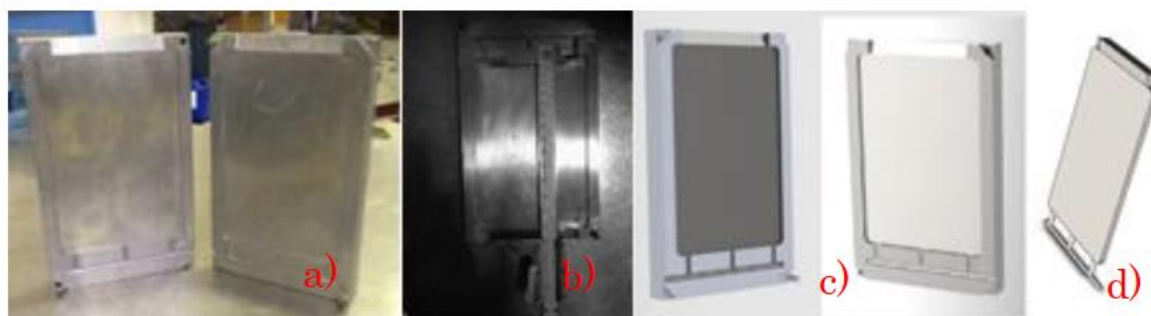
Representação do molde de metal utilizado: a) molde em aço b) e c) medição do molde para obtenção das quantidades de mistura e d) geometria a três dimensões da placa a ser concebida pelo molde. [27]
